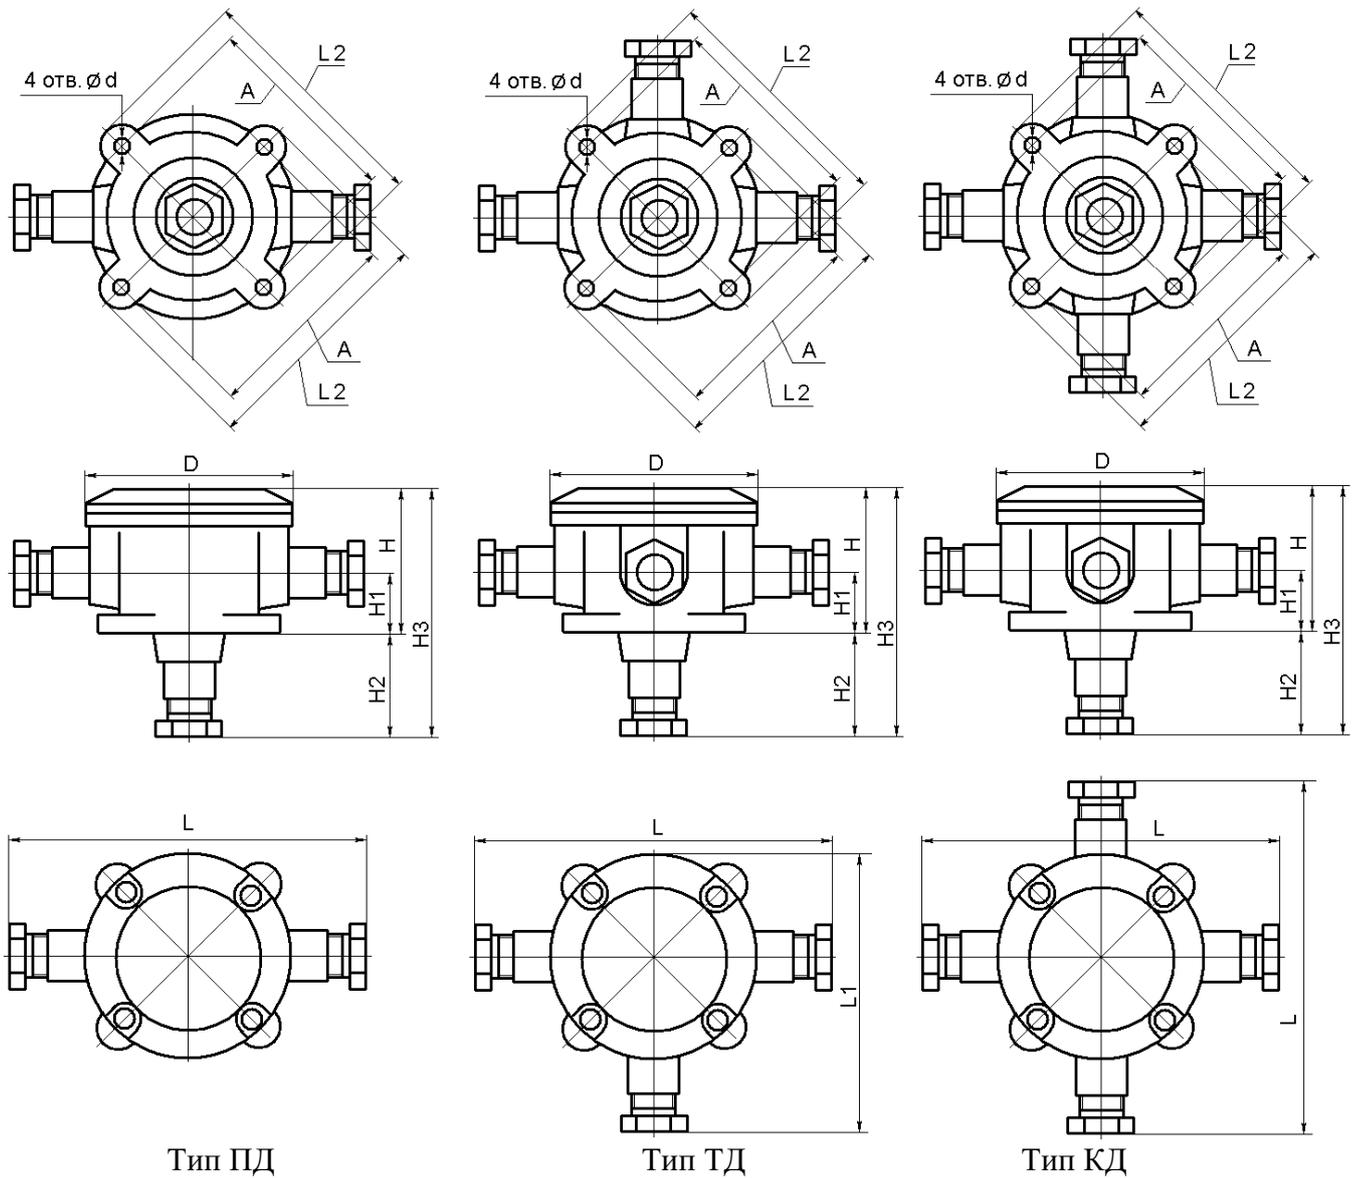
Габаритные, установочные и присоединительные размеры коробок ЕхКСУВ-А с вводным устройством в дне коробки. Остальное – см. рисунок А.3. Приложение А
